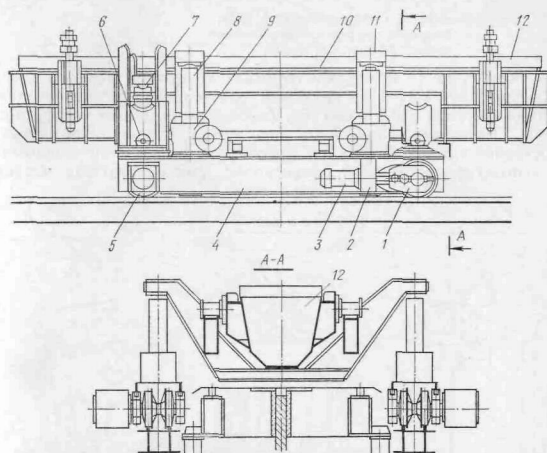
Тележка для промежуточного ковша с прямолинейным движением
